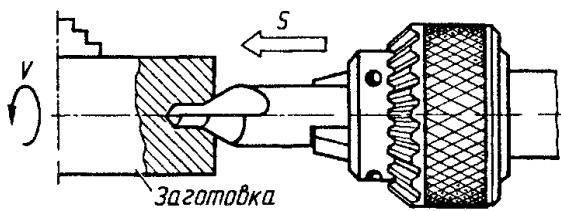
Центрування заготовки вала на токарному верстаті
